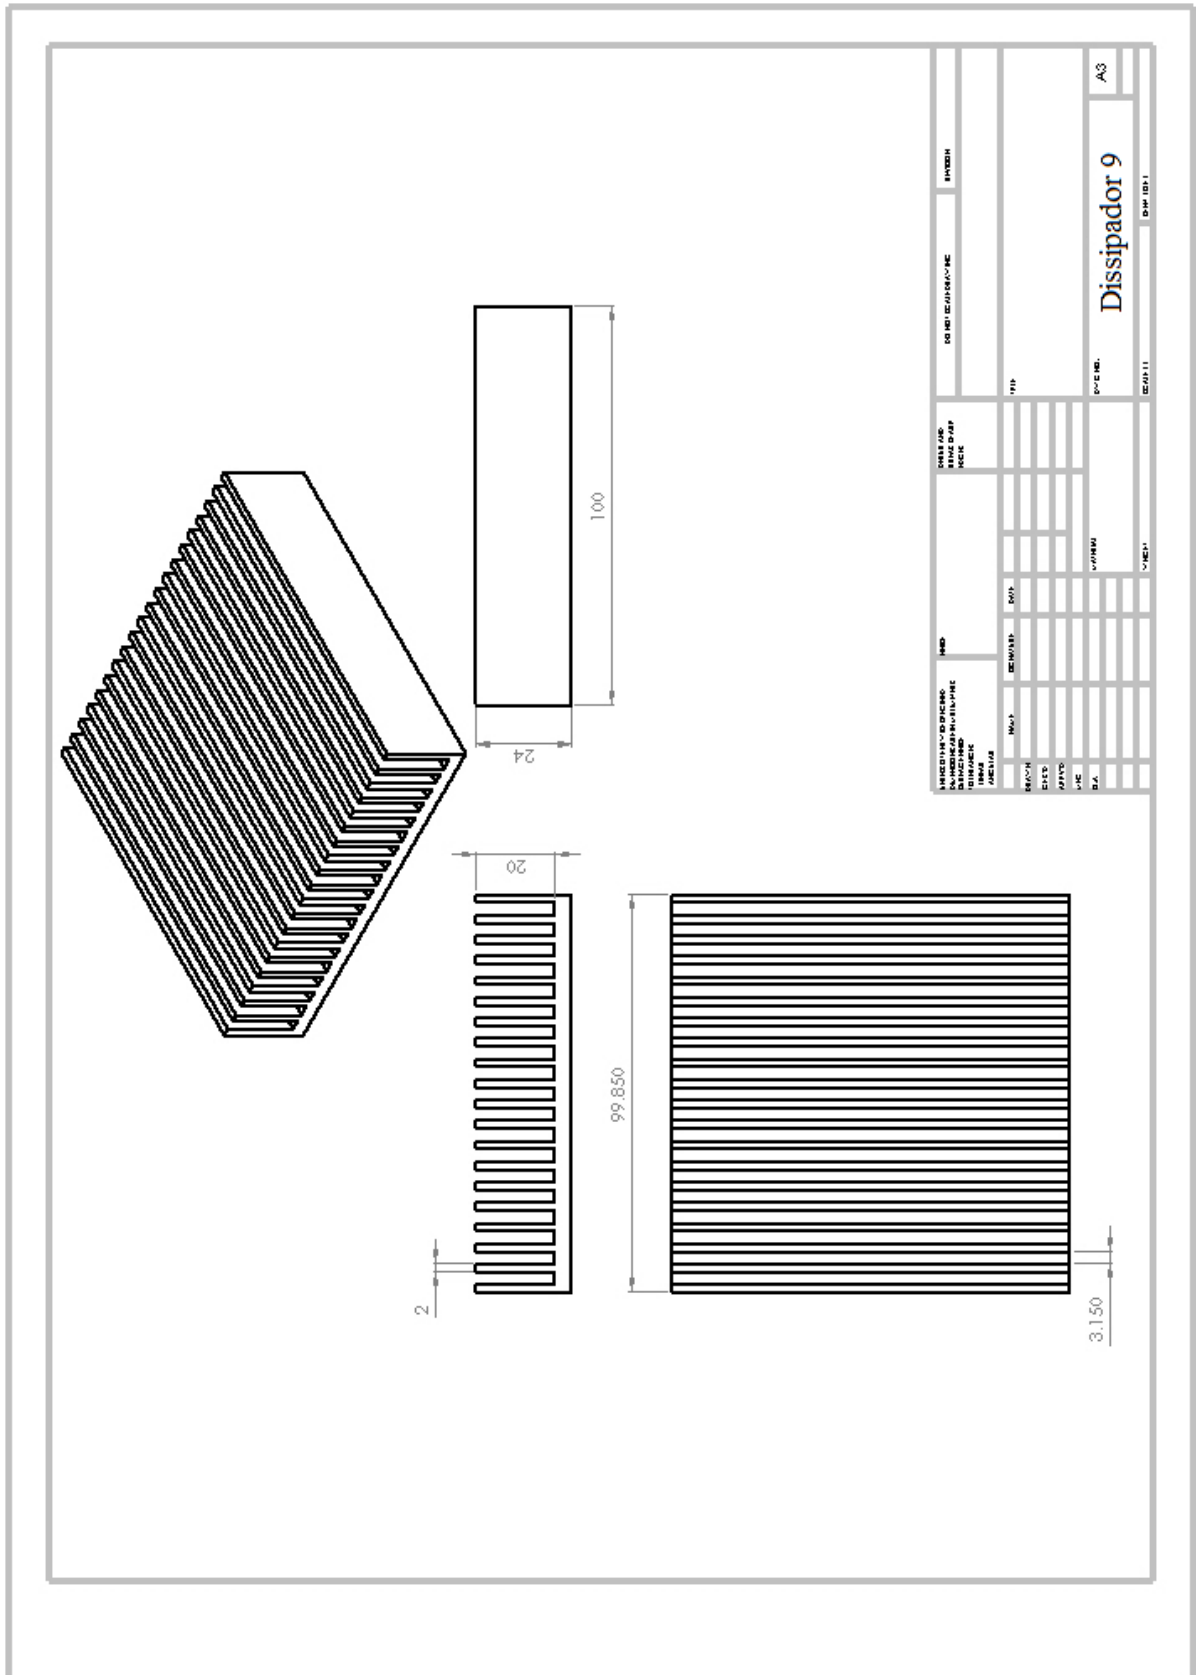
Desenho técnico utilizado para confecção do Dissipador 9.
